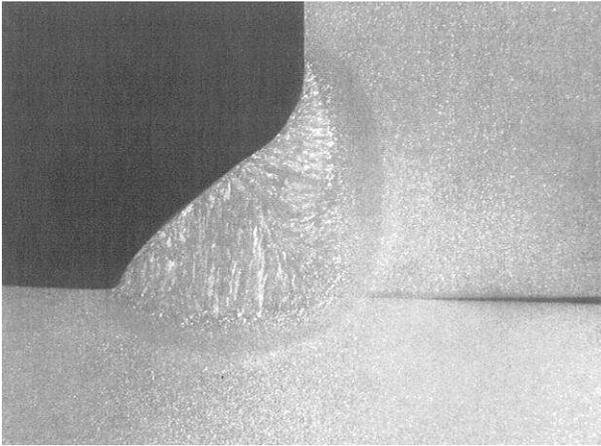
Mit qualifizierten Schweißern und den zurzeit modernsten MIG/MAG-Schweißverfahren erzielt MBH auf wirtschaftliche Art höchste Qualität: Die Schweißnähte zeichnen sich durch sehr sicheren Einbrand, gute Wurzel- und Flankenerfassung aus – Bindefehler sind nahezu ausgeschlossen
